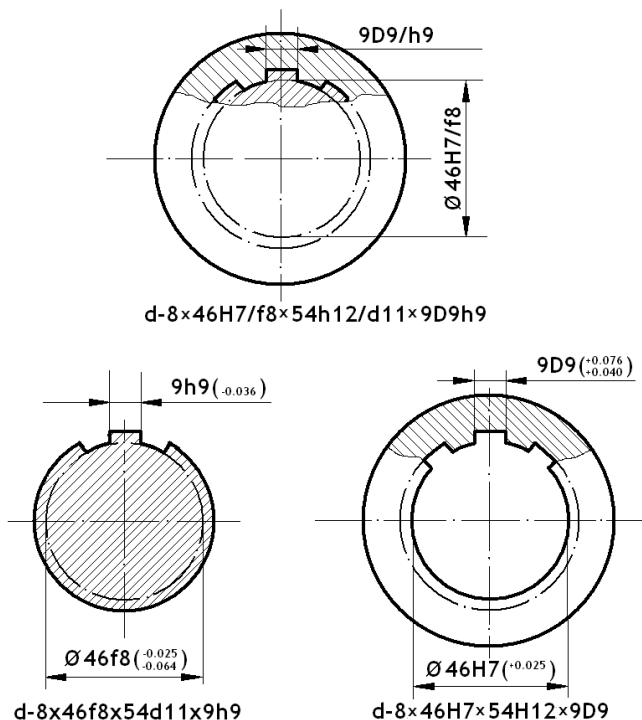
Сборочные и детальные эскизы шлицевого соединения
